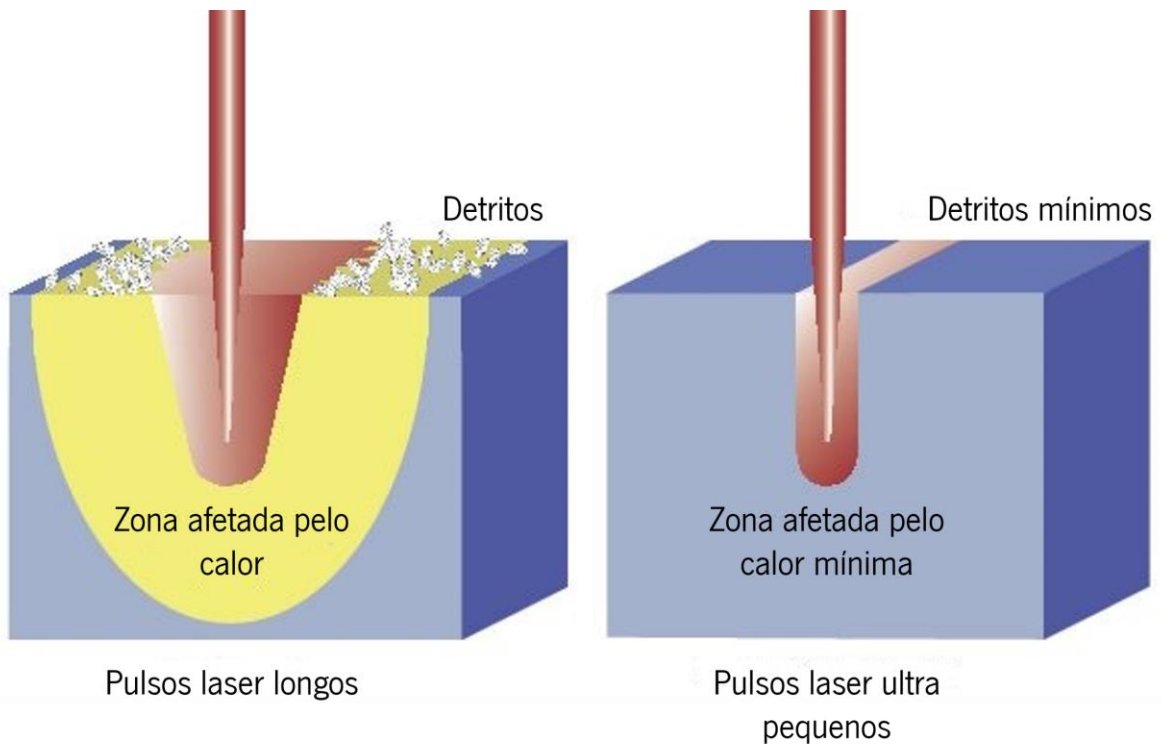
Vantagem da técnica *laser machining* baseada em pulsos laser pequenos (adaptado de [85]).
